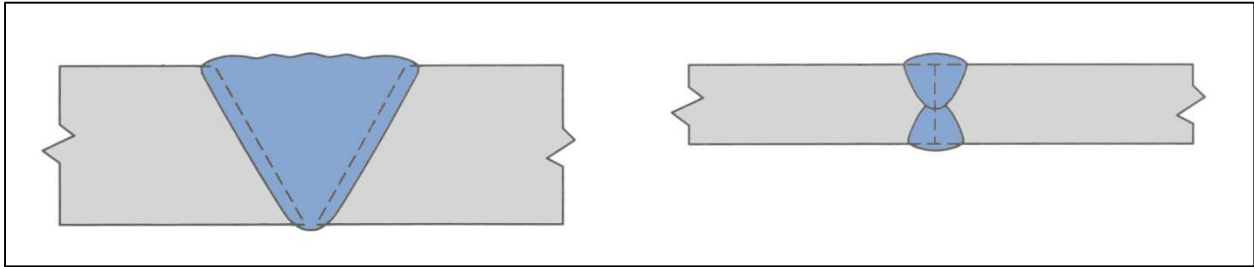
Soldadura de penetración completa. Fuente: American Welding Society, 2019.
